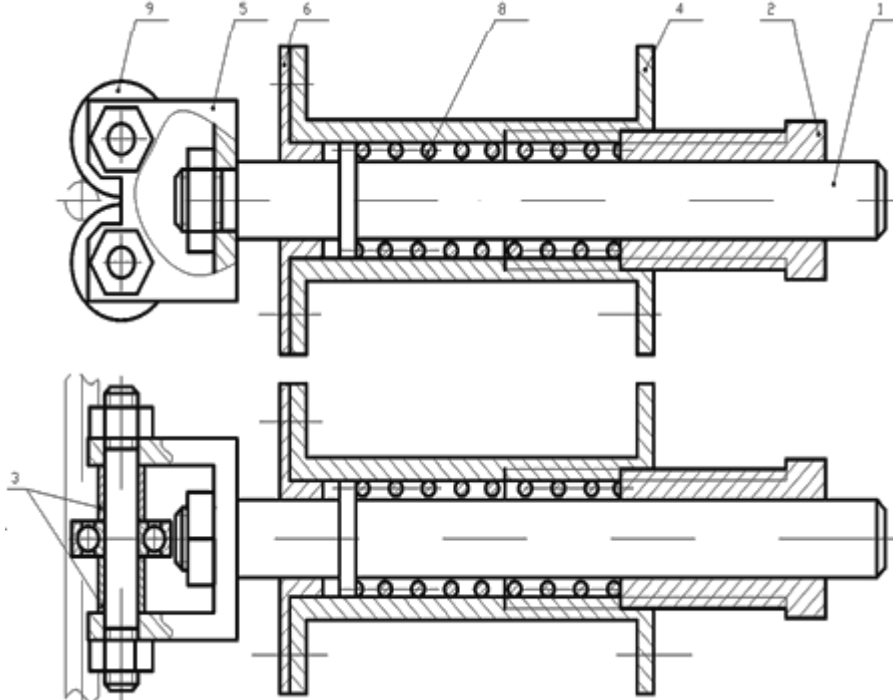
Компенсатор: 1 – вал; 2 – втулка; 3 – втулка распорная; 4 – гильза; 5 – кронштейн; 6 – крышка; 7 – ось; 8 – пружина; 9 – ролики
